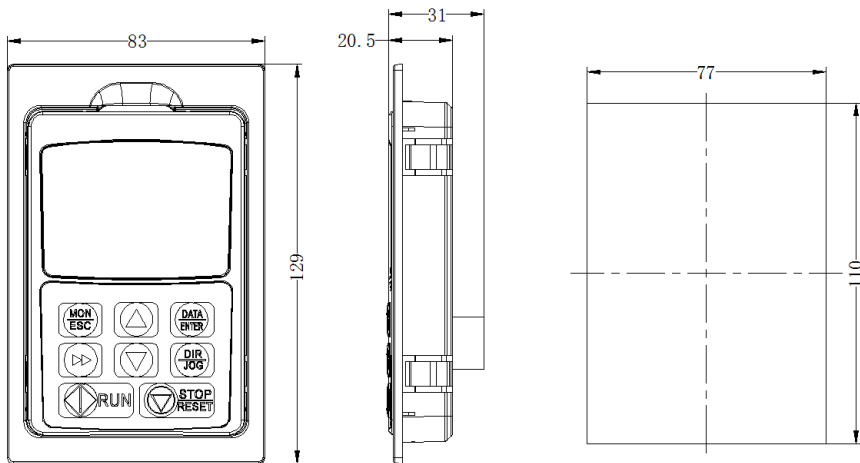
外引键盘的外形尺寸及安装孔尺寸
